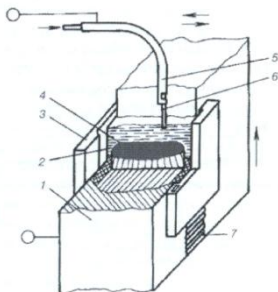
Схема ЭШС: 1, 2- свариваемые изделия; 3 - приставная планка; 4 - флюс; 5 - механизм подачи проволоки; 6 -электрод; 7 - сварной шов
